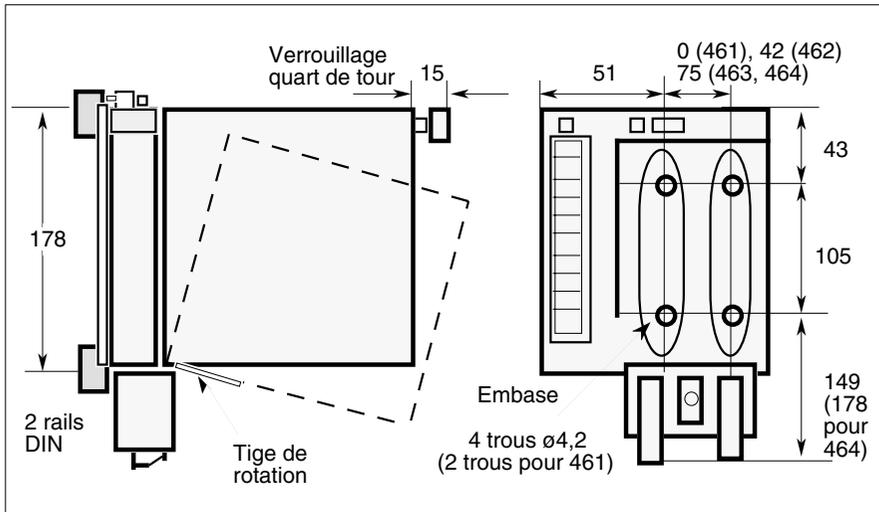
Cotes de fixation sur une paroi verticale (mm)
